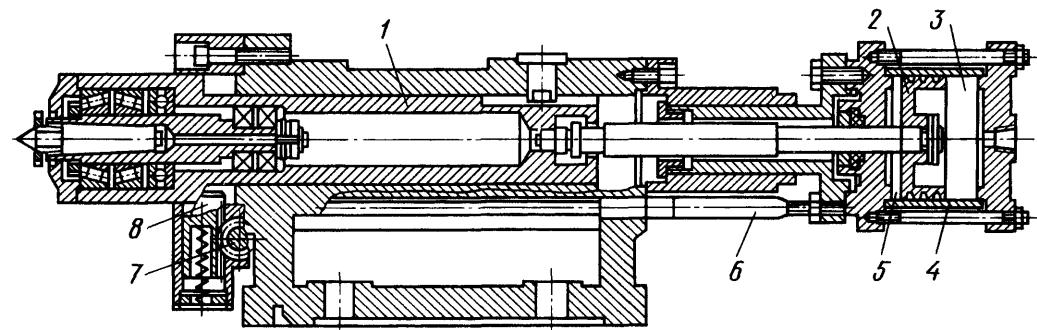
Пиноль задней бабки токарного станка с пневмоприводом
